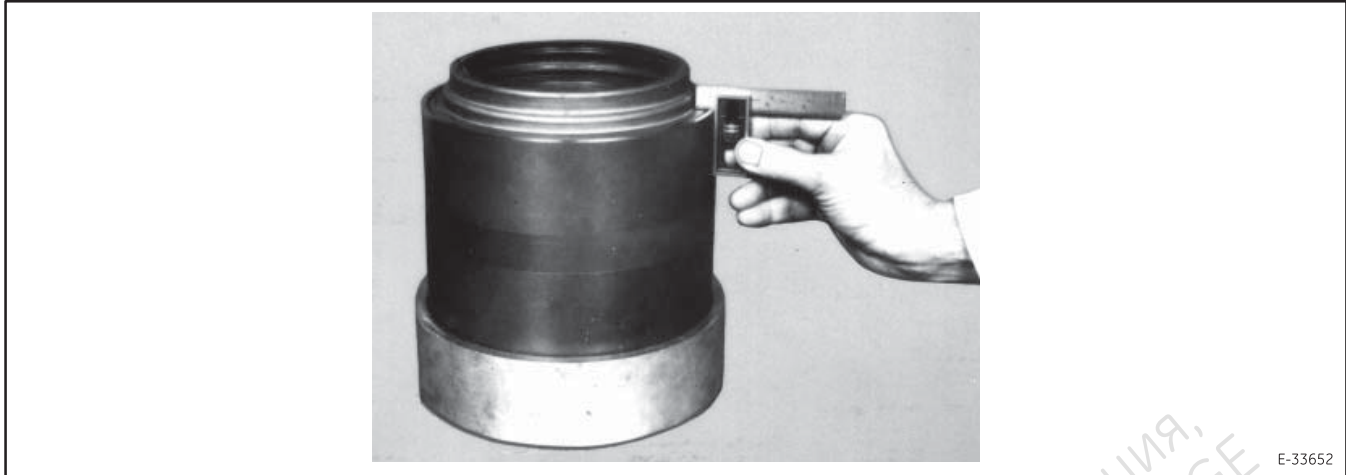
Уплотнение должно быть заподлицо с торцом наружного кольца подшипника, или ниже него.
